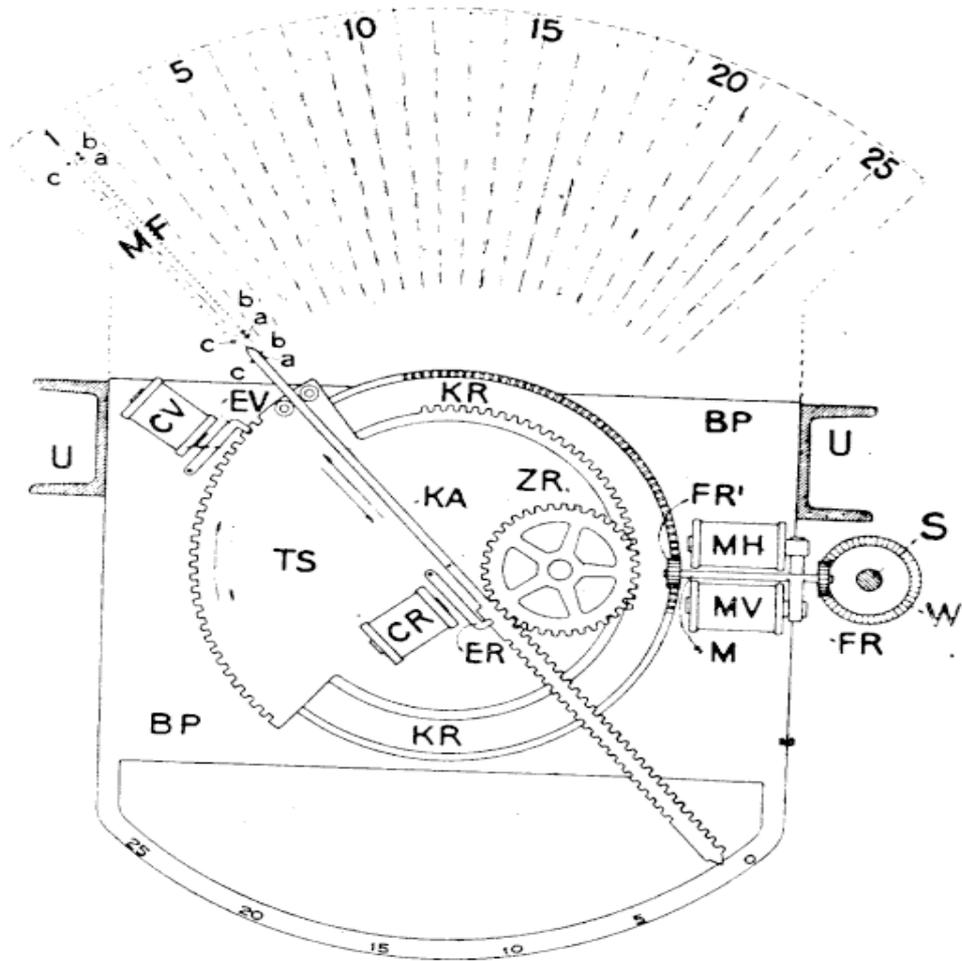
Vue en plan d'un sélecteur et coupe horizontale d'un cadre multiple (disposition schématique).
